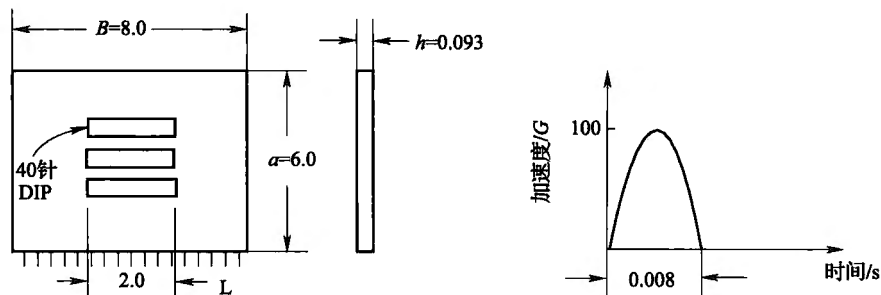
承受 $100G$ 半正弦冲击脉冲的插件式 PCB
